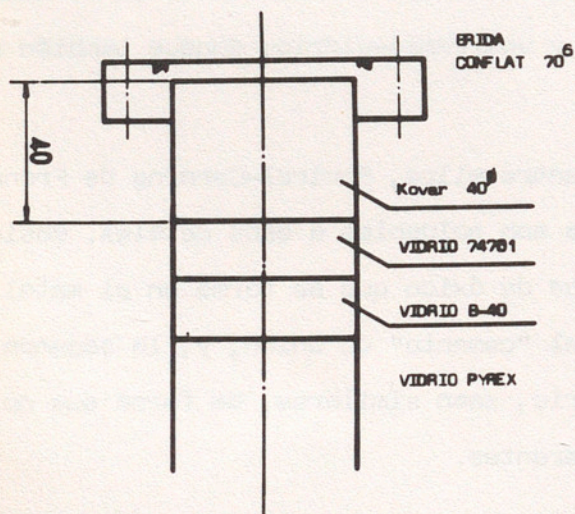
Esquema de una cadena de unión "pyrex-kovar" soldable a brida de cierre de cuchillo de 70 mm φ
